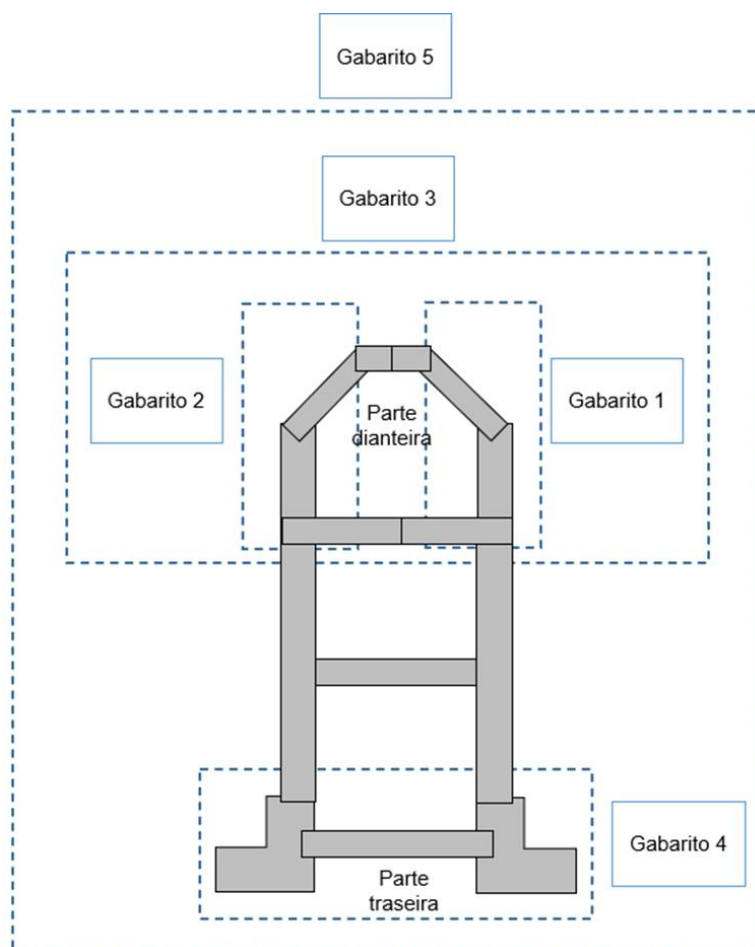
Desenho representativo do chassi de uma máquina agrícola, em vista superior, relacionando o respectivo gabarito para soldagem (Elaboração própria)
